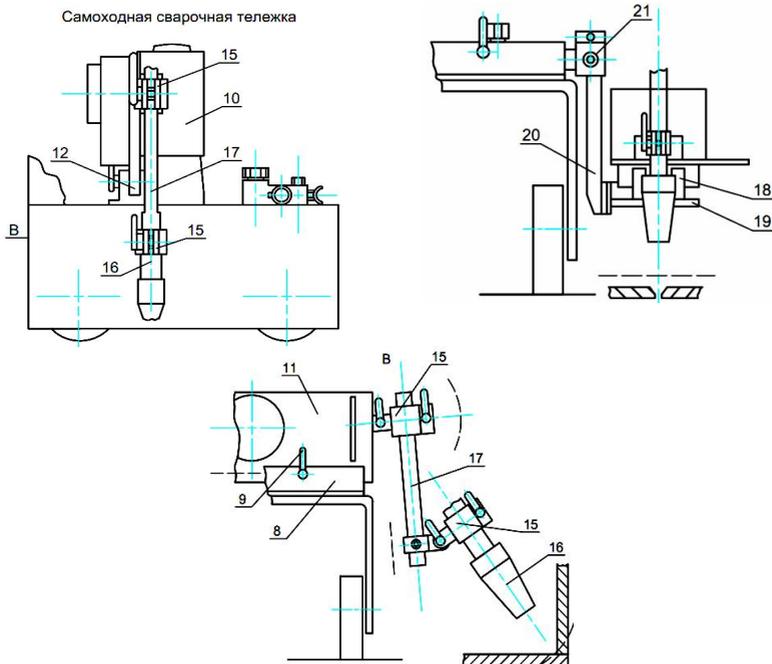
Конструкция самоходной сварочной тележки для автоматизированного мобильного технологического комплекса сварки
